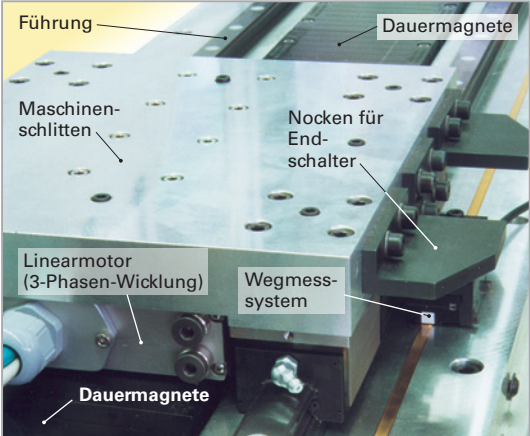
Linearmotor als Direktantrieb für einen Maschinentisch
